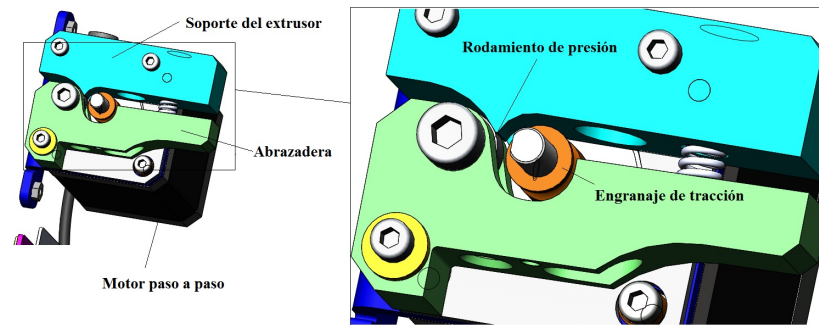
Diseño CAD del extrusor de la impresora *Sigma* completo.
